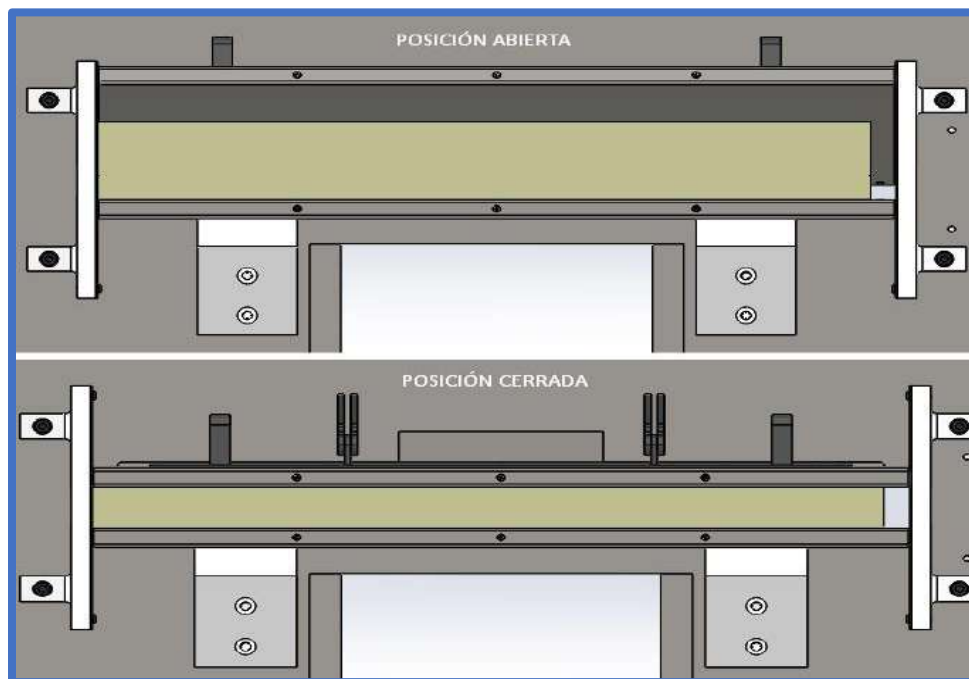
Posición abierta de la “Pared Pivoteante” (Imagen Sup) – Posición cerrada de la “Pared Pivoteante” (Imagen Inf)
